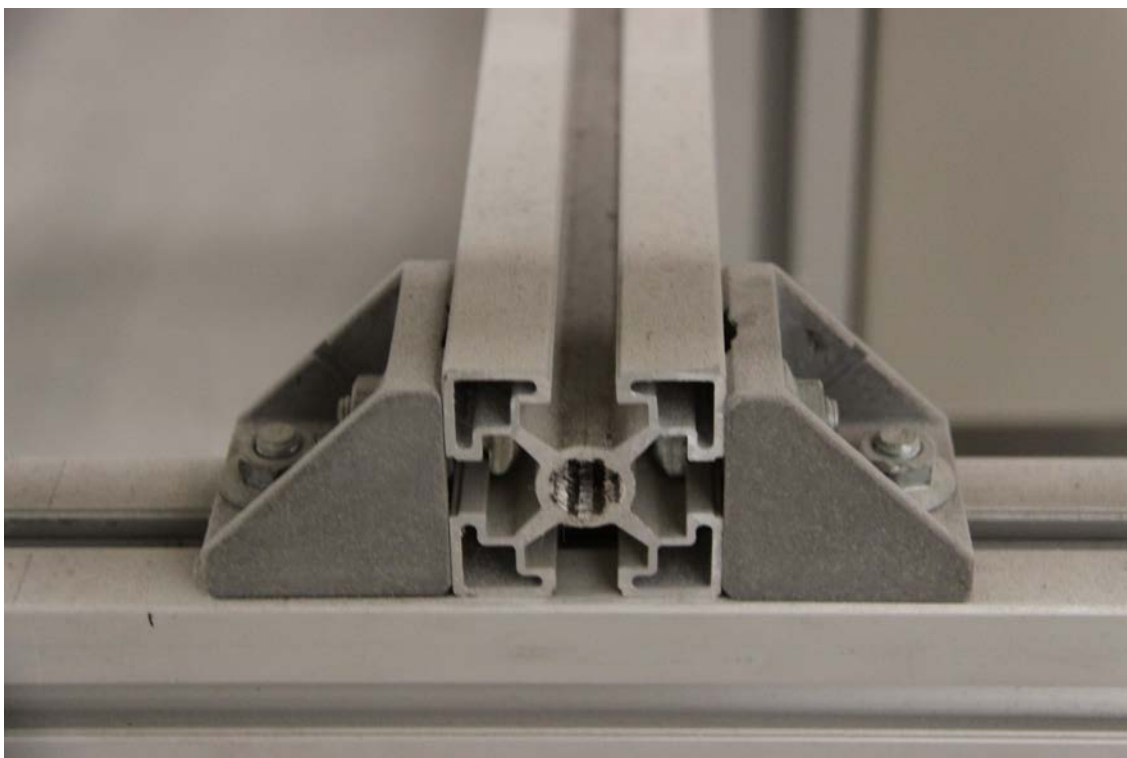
Pormenor do equipamento de abastecimento de pré-formas para a Pultrusão Híbrida – Perfil usado e ligações
